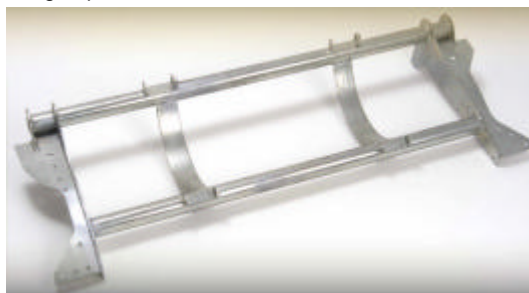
Constructions soudées du groupe Huissel pour la construction automobile
